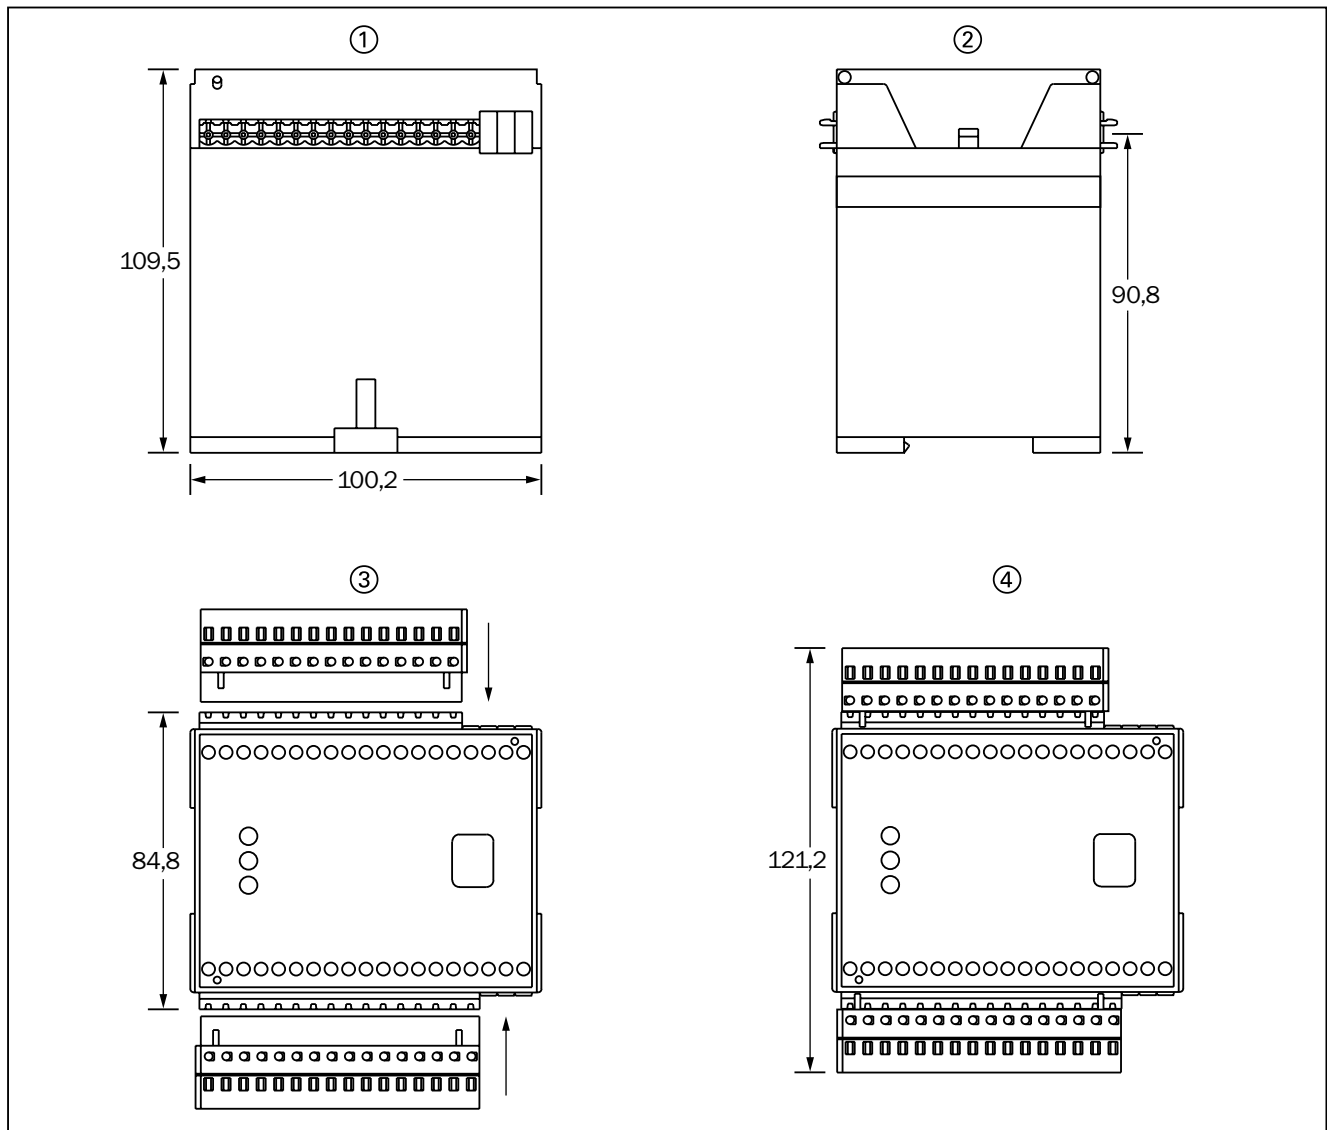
Cotes d'encombrement des LE 20-Inhibition avec bornier à vis
